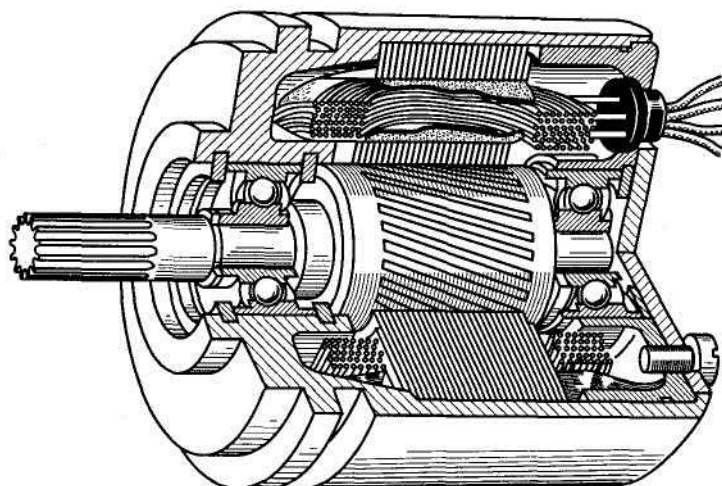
Асинхронный исполнительный двигатель сквозной конструкции
